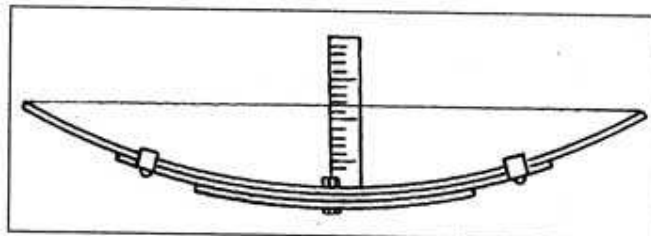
Проверка стрелы прогиба дополнительной рессоры
